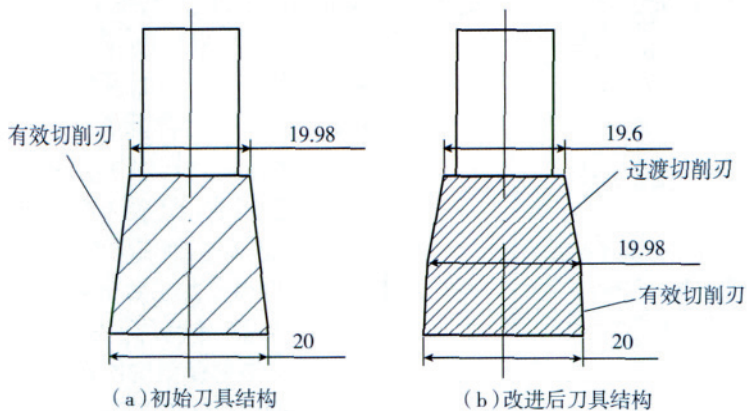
薄壁结构(侧壁)铣削用锥度立铣刀结构示意图
